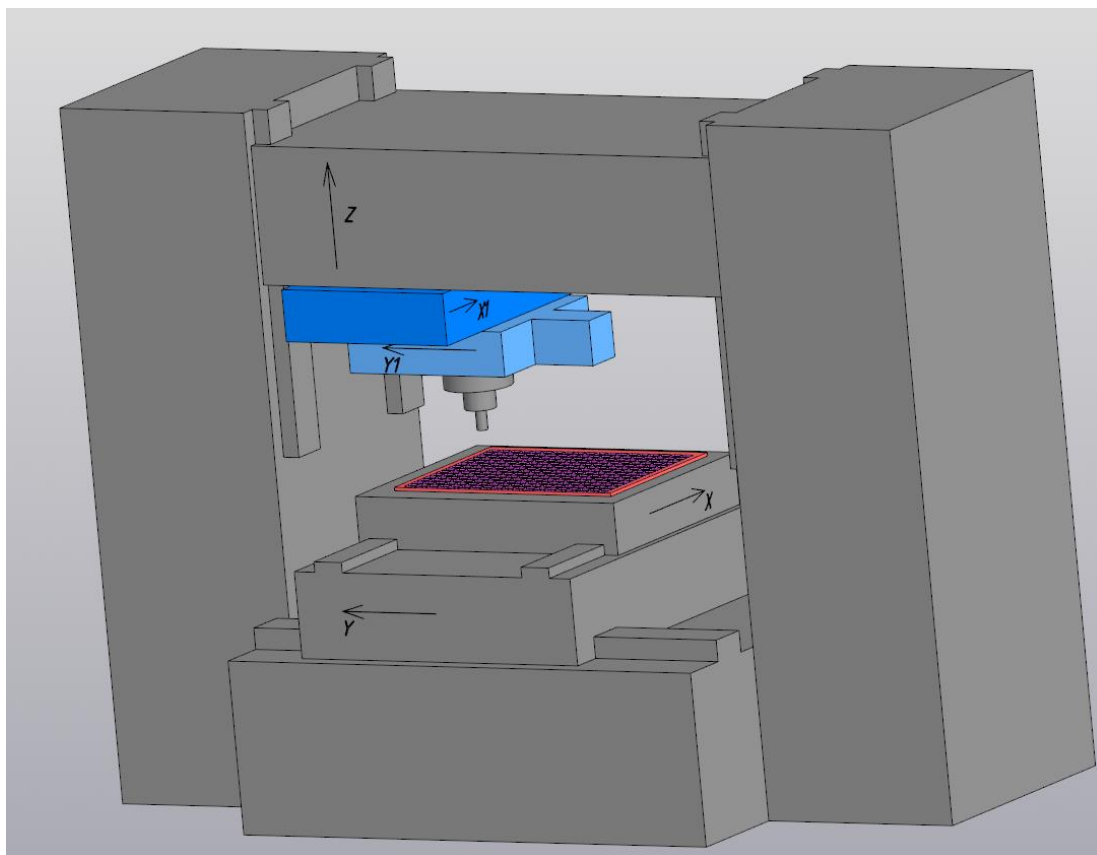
Пример компоновки портального фрезерного станка
